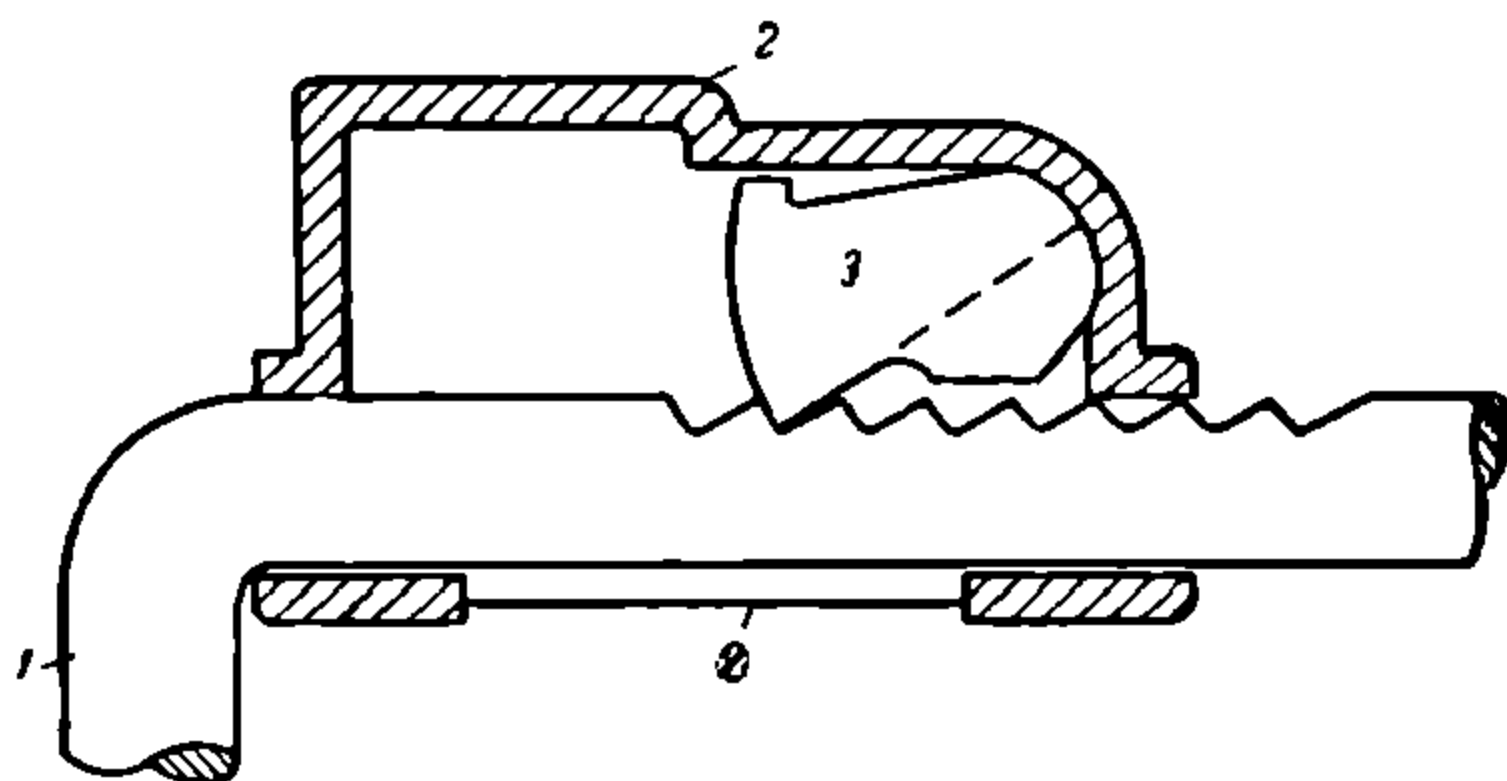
Общий вид приспособления марки «Рояль» для регулировки рычажной передачи.
